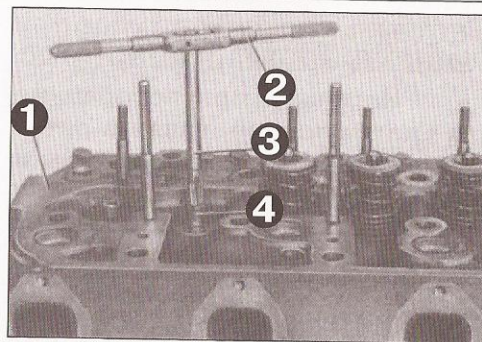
Частичный обзор головки блока цилиндров, показывающий процесс расточки направляющей втулки клапана.
